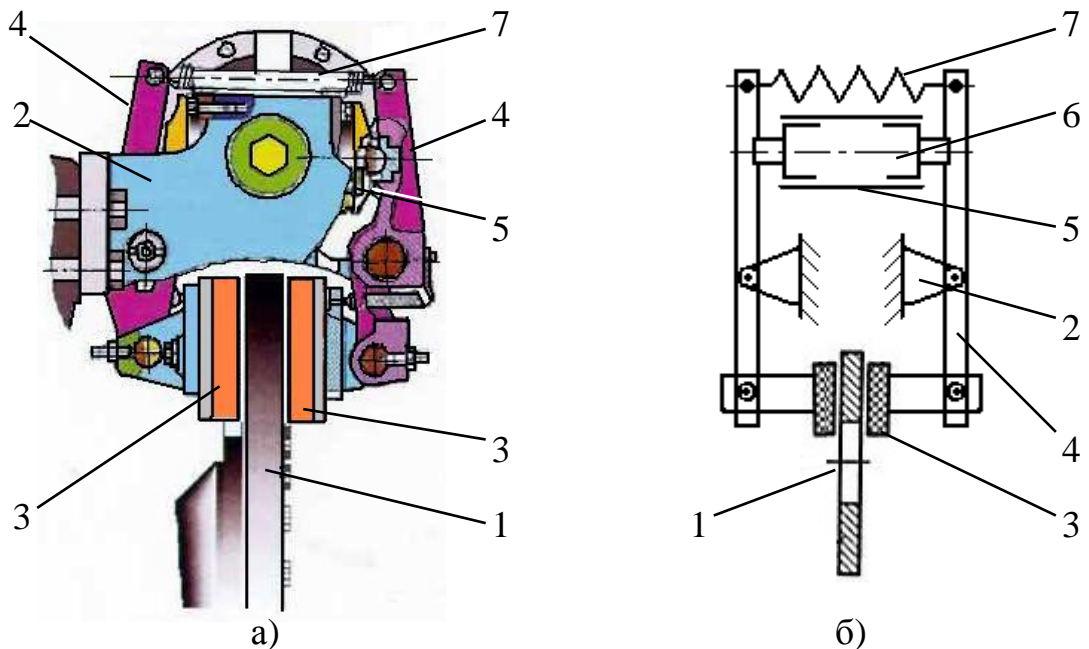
Дисковый тормозной механизм с качающейся скобой: а – конструкция, б – схема; 1 – тормозной диск; 2 – суппорт; 3 – тормозные колодки; 4 – рычаги; 5 – цилиндр; 6 – поршни; 7 – возвратная пружина
